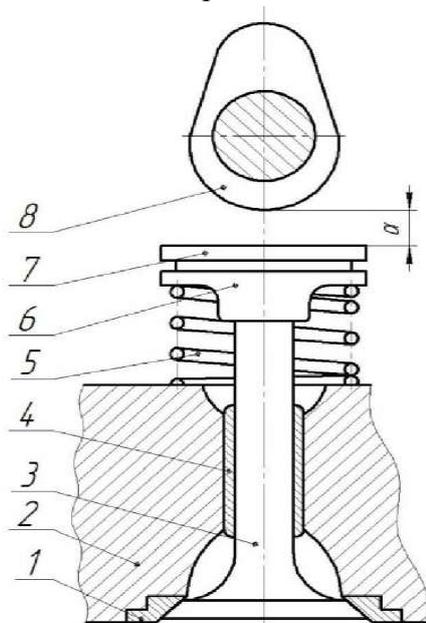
Определение теплового зазора в клапанном приводе двигателя с верхним расположением распределительного вала 1 - Клапанное гнездо; 2 - Крышка цилиндра; 3 - Клапан; 4 - Направляющая втулка; 5 - Пружина клапана; 6 - Замковая тарелка; 7 - Упорная тарелка; 8 - Распределительный вал замком; а - Тепловой зазор в клапанном приводе
